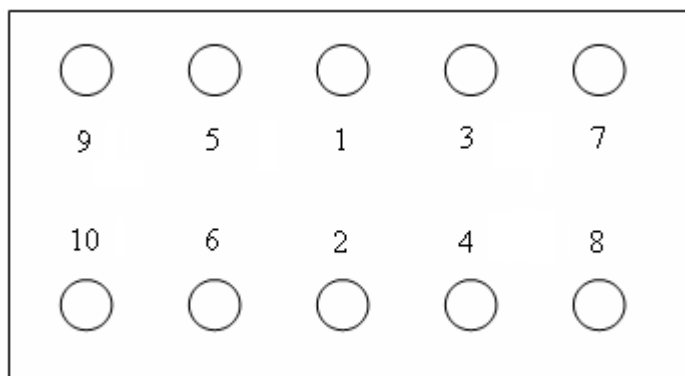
Схема затяжки гаек коренных подшипников двигателя Д-50.
